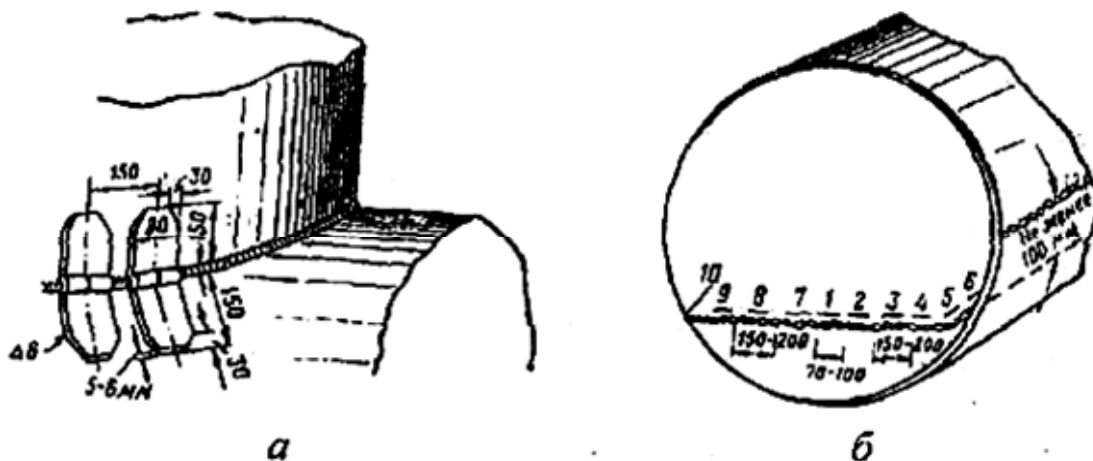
Ремонт резервуаров и цистерн: а - горловины; б - обечайки и днища; 1... 10 - последовательность сварки обратноступенчатым способом
